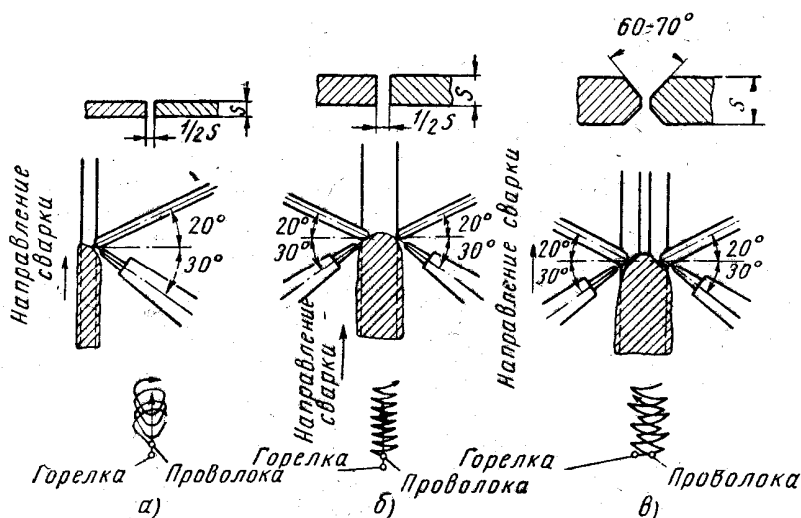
Схемы сварки сквозным валиком при толщине (S) металла:
